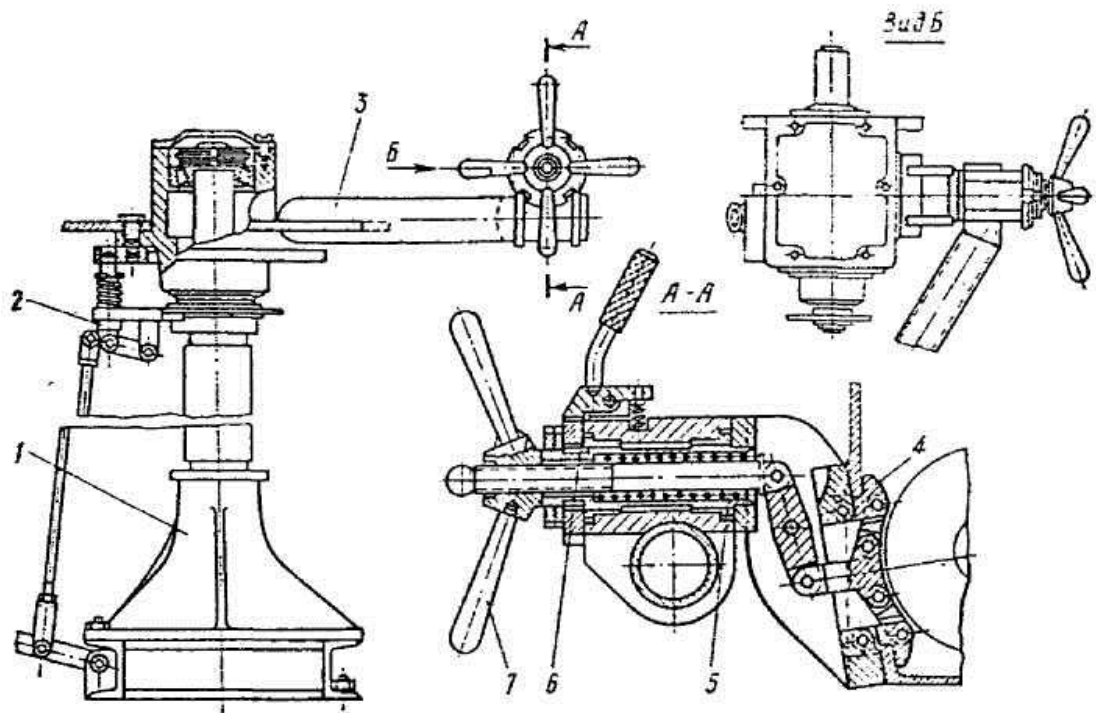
Стенд для остаточного розбирання коробок передач, модель 703-1
